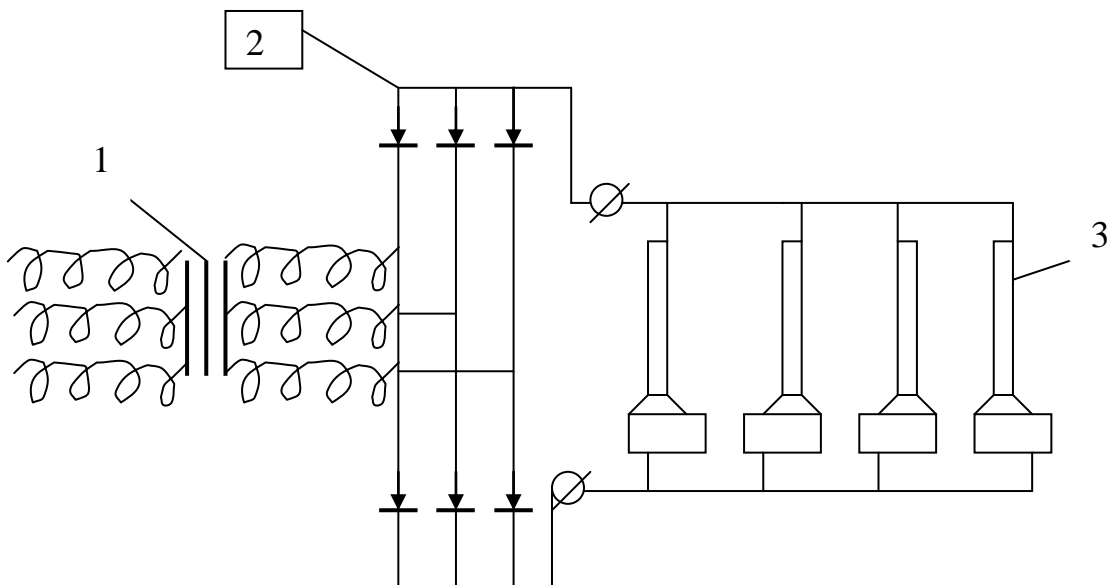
Принципова схема багатопостового зварювального випрямляча з баластними реостатами: 1 – понижуючий зварювальний трансформатор зі збільшеним магнітним розсіянням; 2 – блок напівпровідникових вентилів; 3 – баластні реостати.
